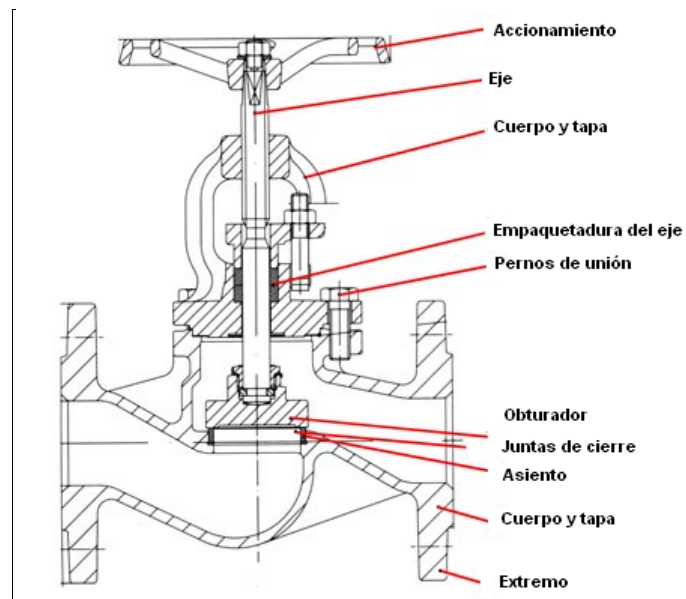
Partes Principales de una Válvula (Válvula de Globo). [6]
